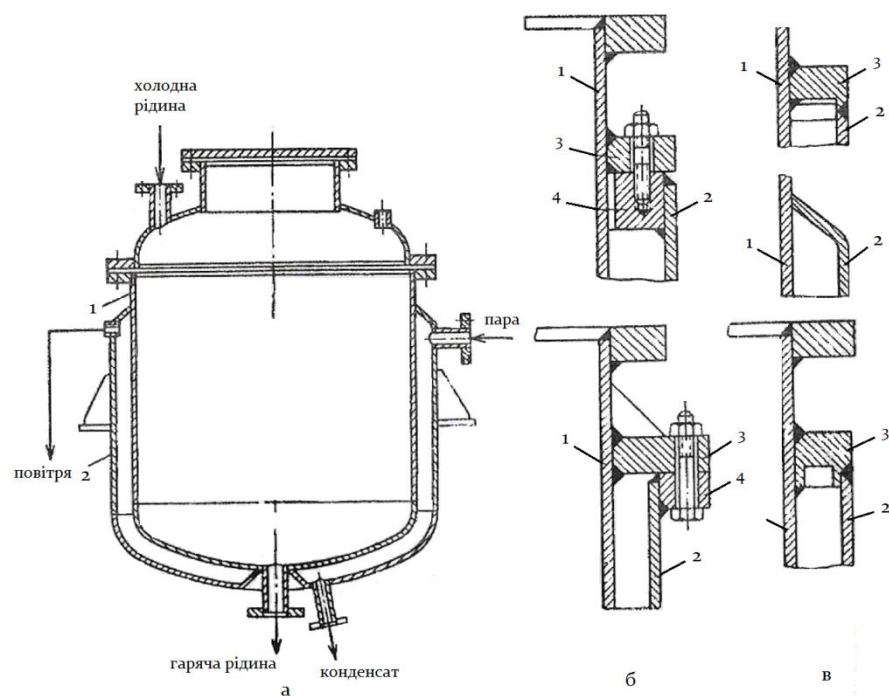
Апарат із нагрівальною оболонкою (а) і способи її приєднання (б - фланцеве; в - зварене): 1 - корпус апарату; 2 - нагрівальні оболонки; 3 - кільця; 4 - фланці.
